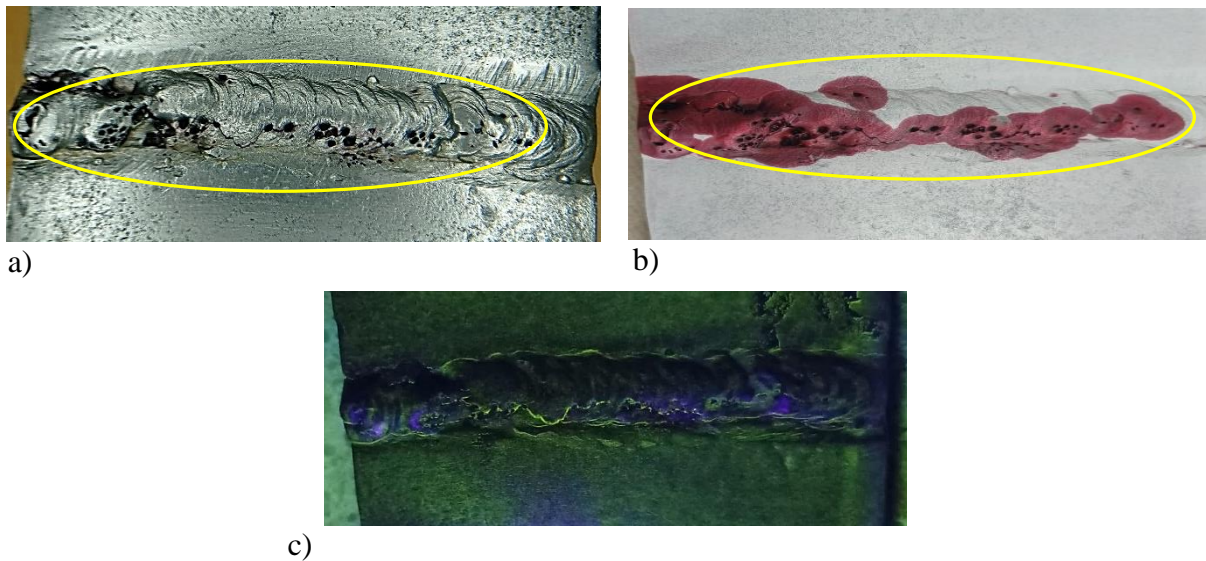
Muestra M9. Acero ASTM A36 (Muestra Diseñada Para Generación De Grieta)
